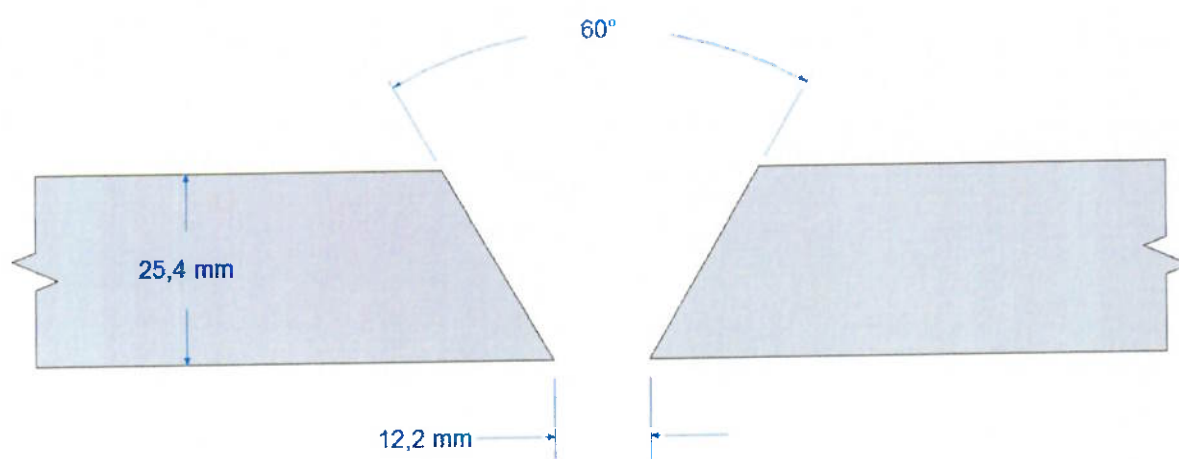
3 - Formato das juntas a serem soldadas pelo processo EGW.
